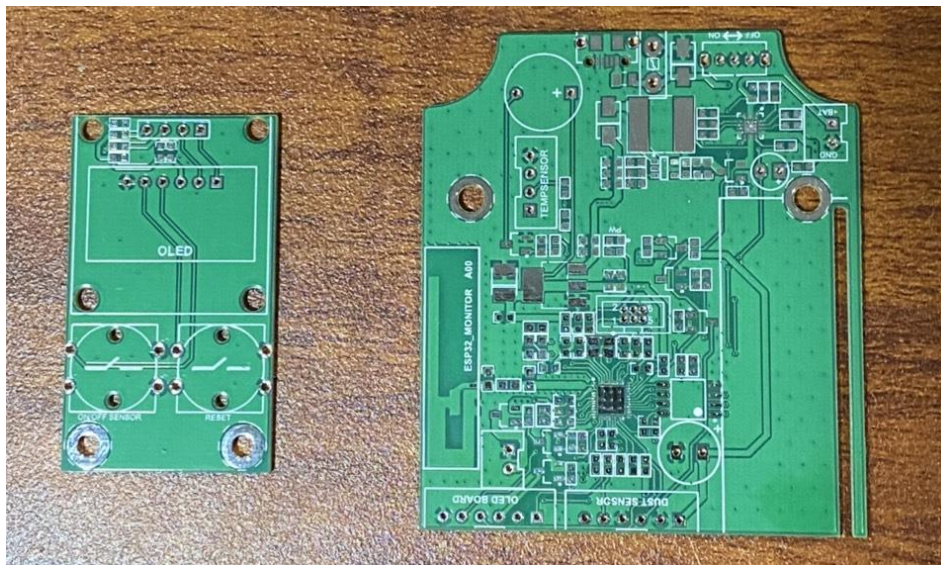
Hình ảnh mặt trước của PCB OLED
